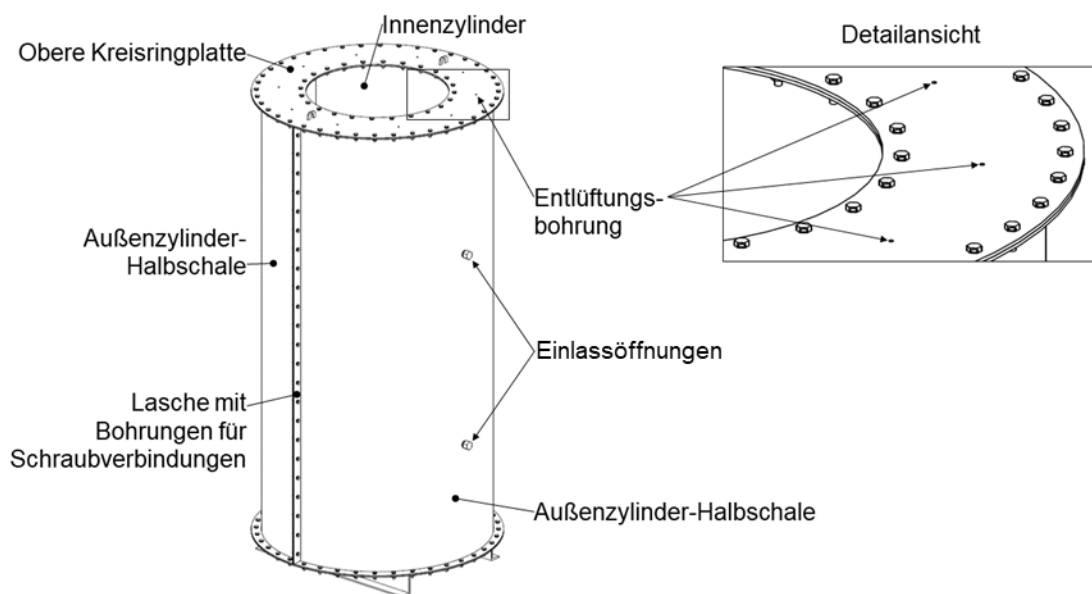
3D-Ansicht des geschlossenen Formwerkzeugs für die Mantelwärmedämmung
